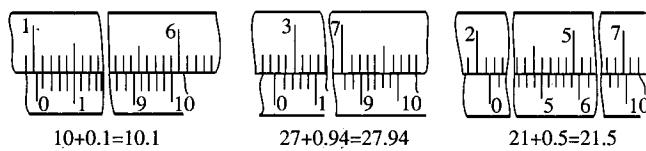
游标读数值为 0.02 mm 游标卡尺读尺寸方法
